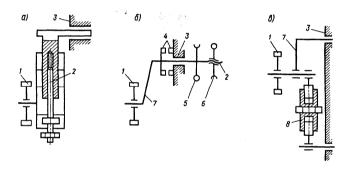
Типы механизмов натяжения гусениц: 1 — направляющее колесо; 2 — винтовой механизм; 3 — корпус машины; 4 — фиксирующие гребенки; 5, 6 — червячные пары; 7 — кривошип; 8 — винтовая стяжка
